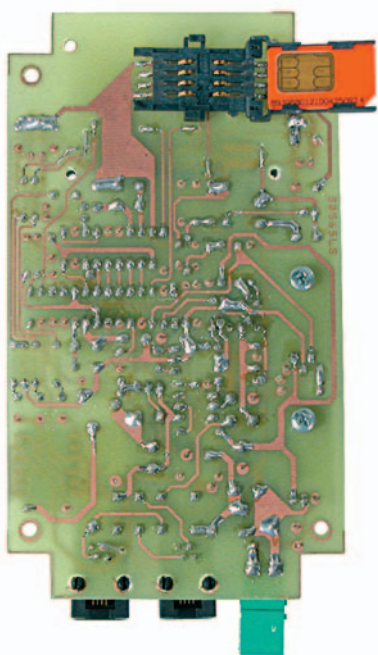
Photos d'un des prototypes de la platine du téléphone fixe-GSM, face soudures, où est monté le porte-SIM (ci-dessus: détail).
